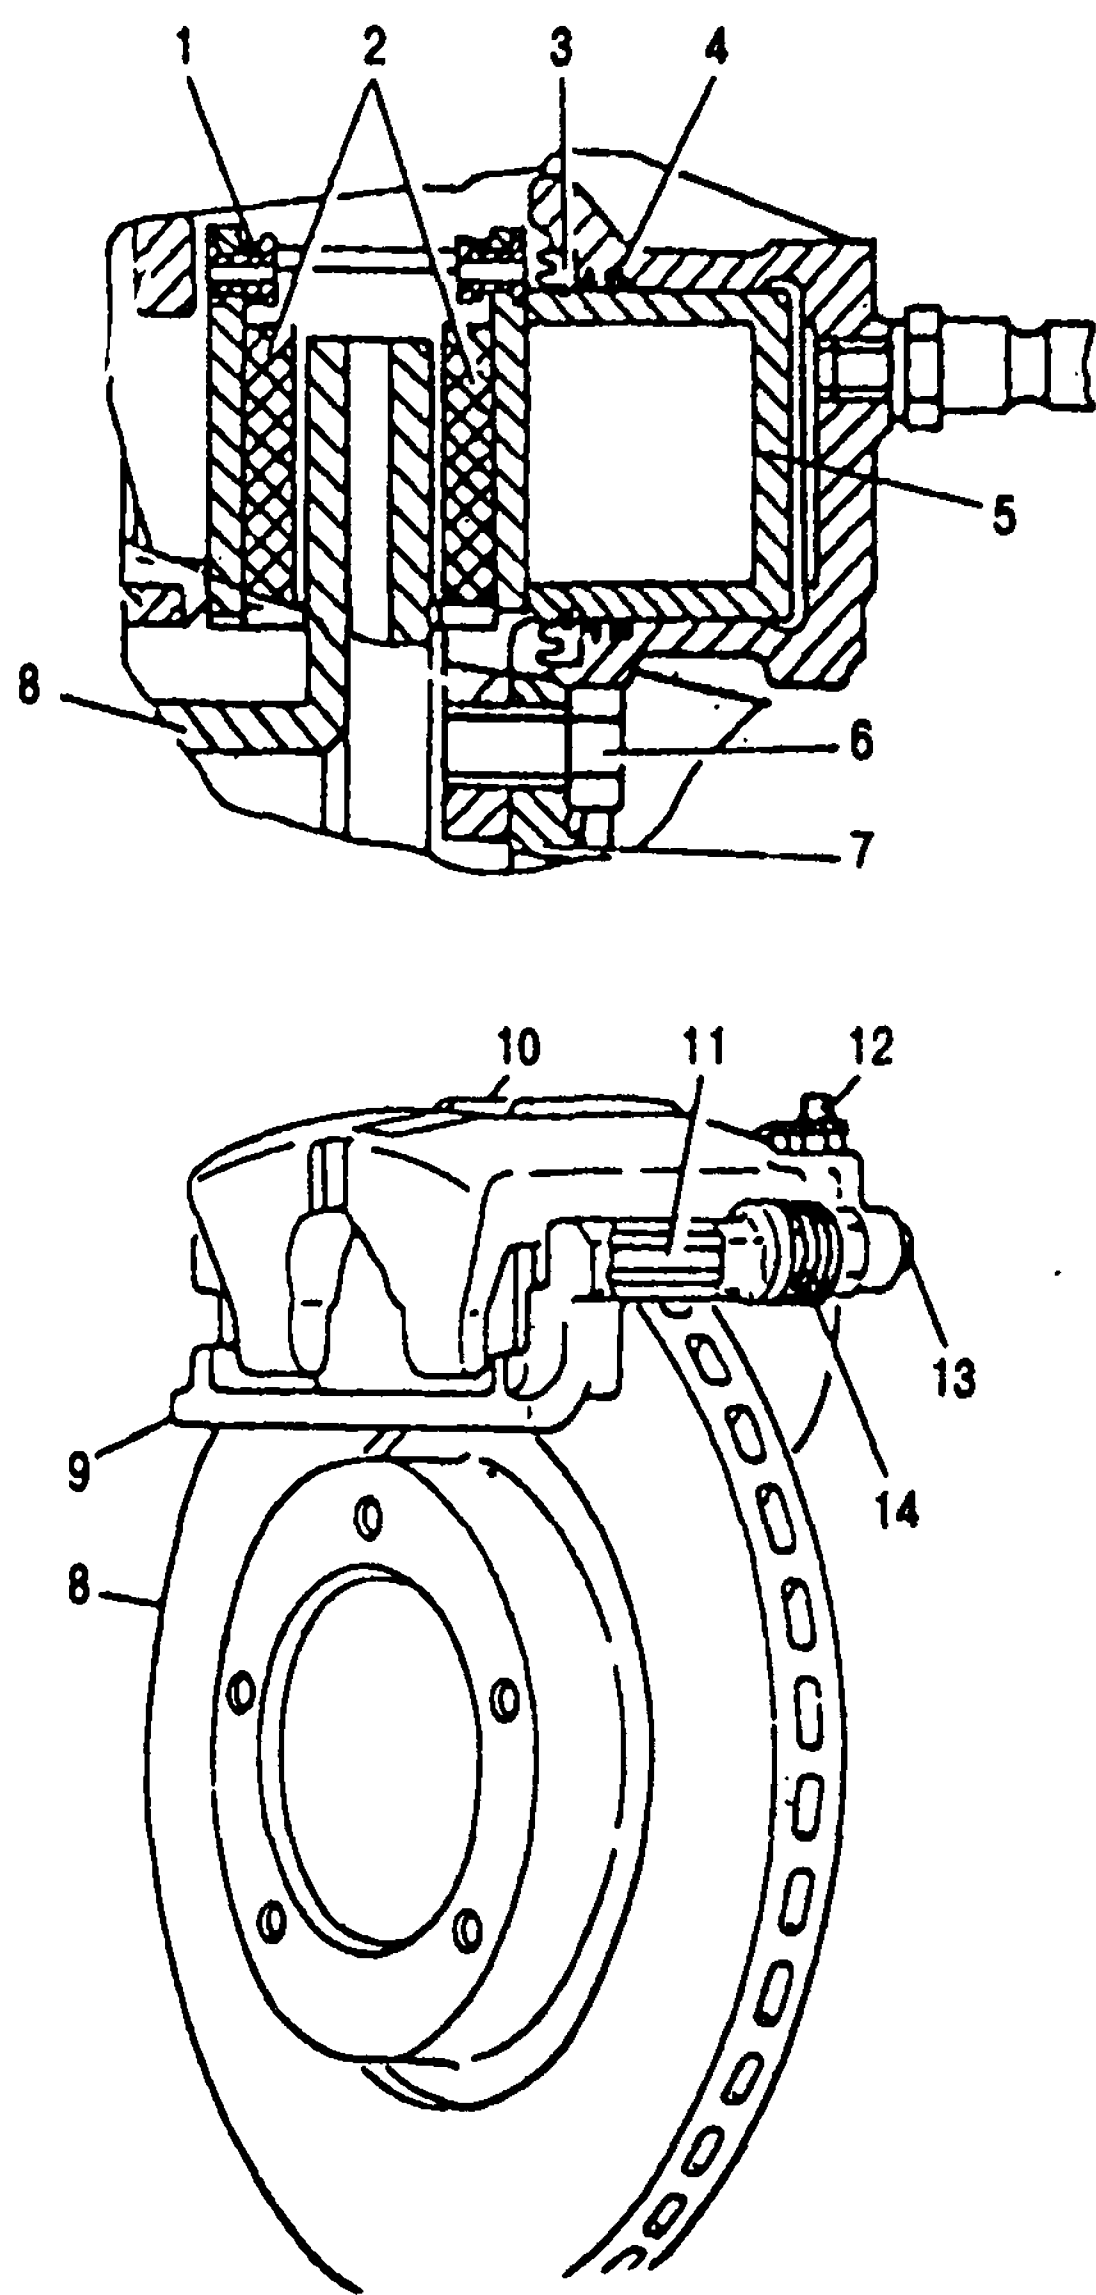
Тормозной механизм передних колес: 1 - пружина колодки; 2 - тормозная колодка; 3 - защитный чехол поршня; 4 - уплотнительное кольцо; 5 - поршень; 6 - болт; 7 - поворотный кулак; 8 - тормозной диск; 9 - основание скобы; 10 - корпус скобы; 11 - направляющий палец; 12 - клапан прокачки с защитным колпачком; 13 - болт крепления пальца; 14 - защитный чехол пальца
